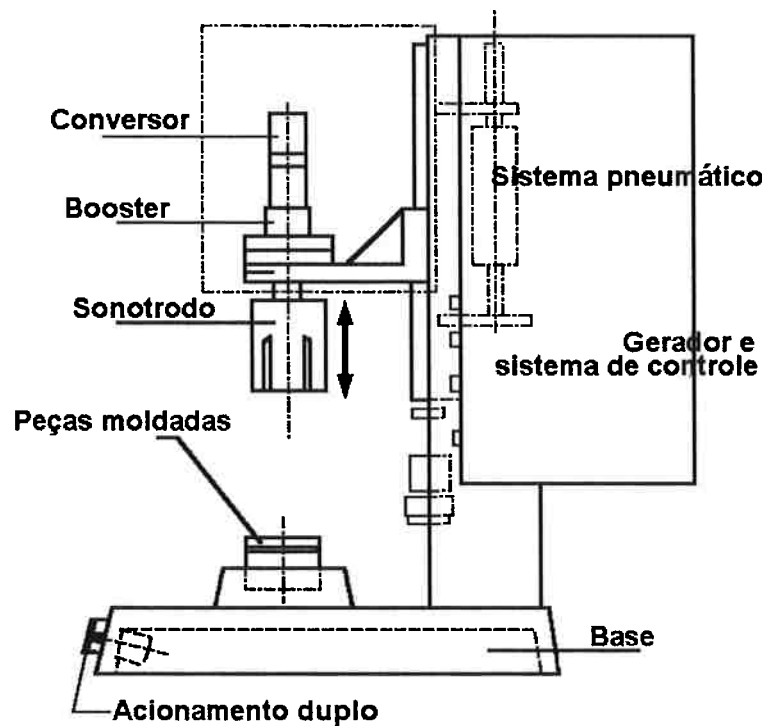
Representação esquemática do equipamento de soldagem por ultra-som
